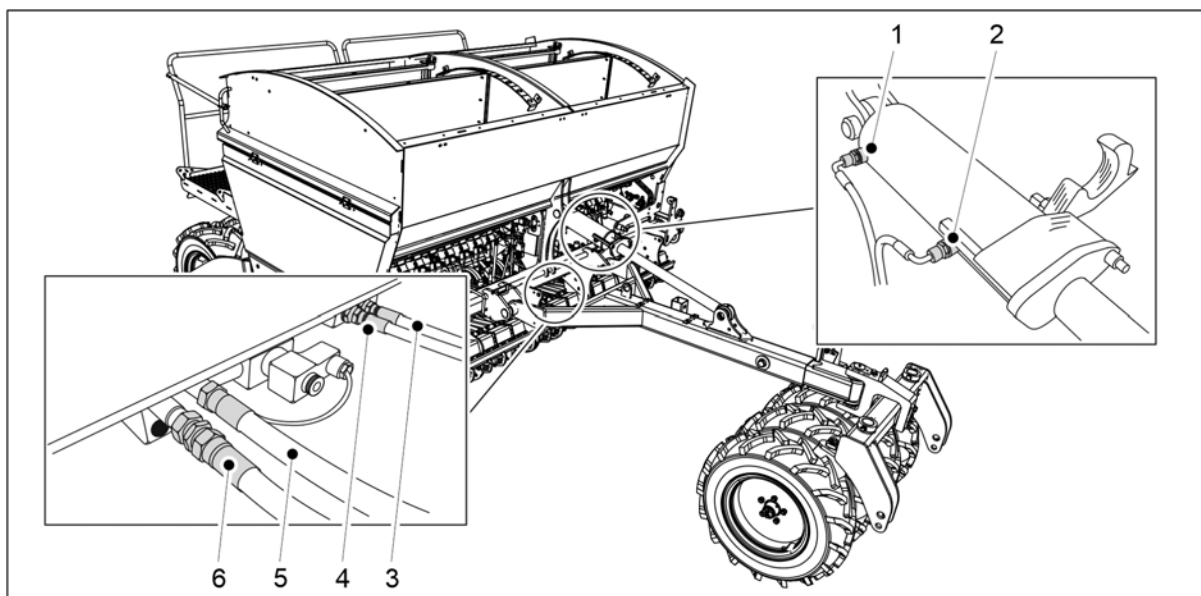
37. Montáž kolového pěchu
